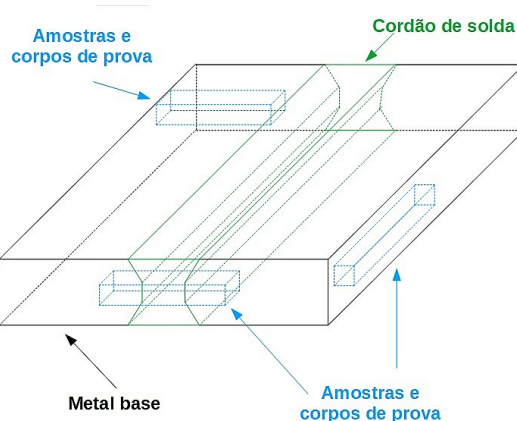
Esquema de retirada de amostras e corpos de prova das placas e juntas soldadas. Obs.: As placas/junta soldada foram analisadas no estado bruto de fusão.
